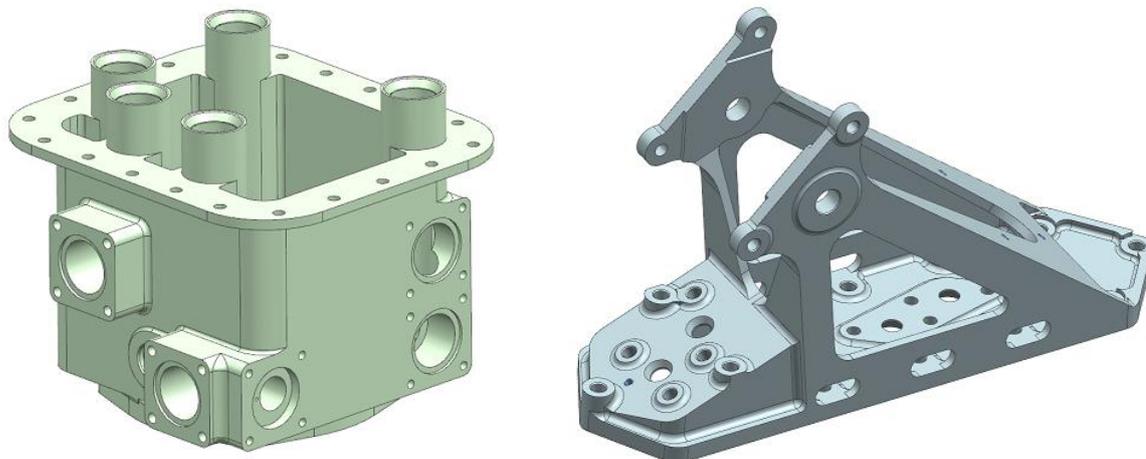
Заготовка (а) из алюминиевого сплава АК6 (габарит 180×160×80 мм) и деталь «качалка» (б)
